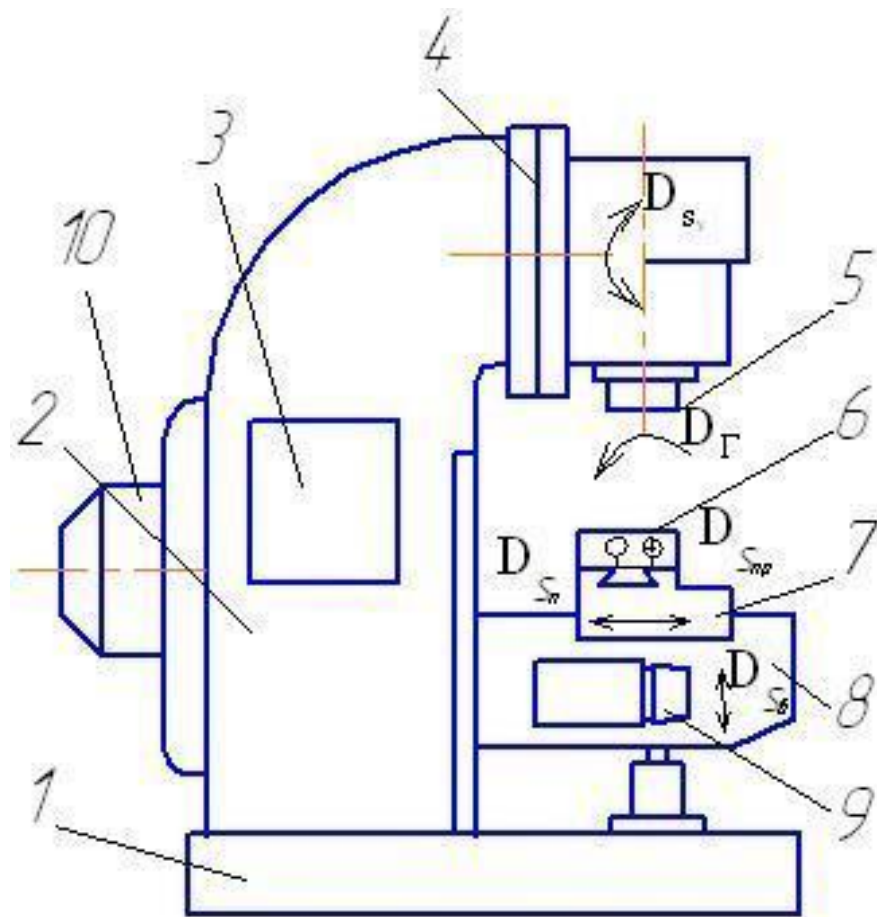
Основные узлы вертикально-фрезерного станка модели 6Т10
